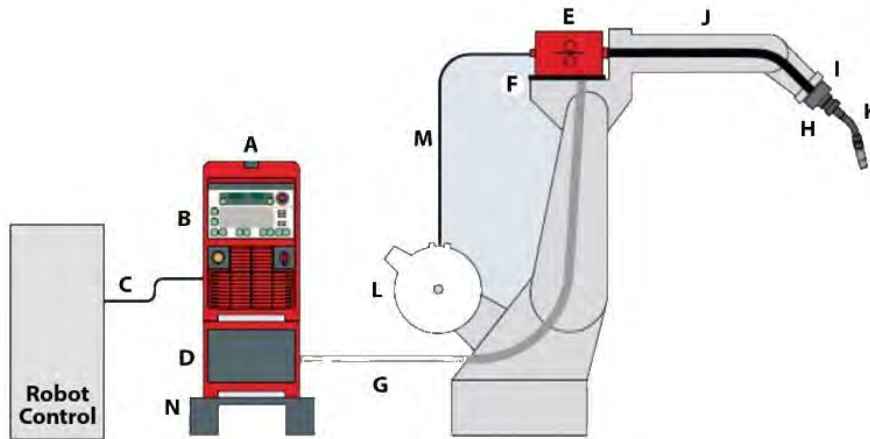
Componentes de una fuente de soldadura, Fuente: Fronius.com
